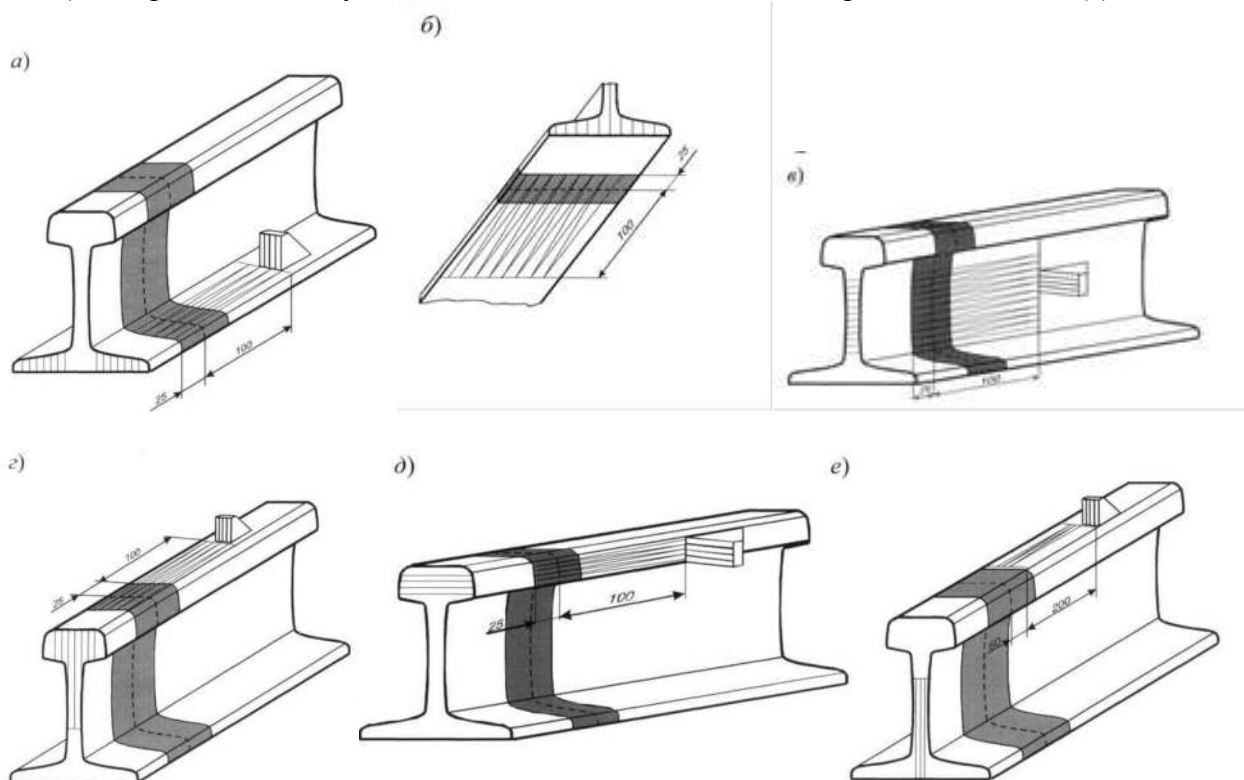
Схемы прозвучивания сварного стыка рельса (штриховой линией показана зона сварного стыка, озвучиваемая при выполнении каждой операции).
